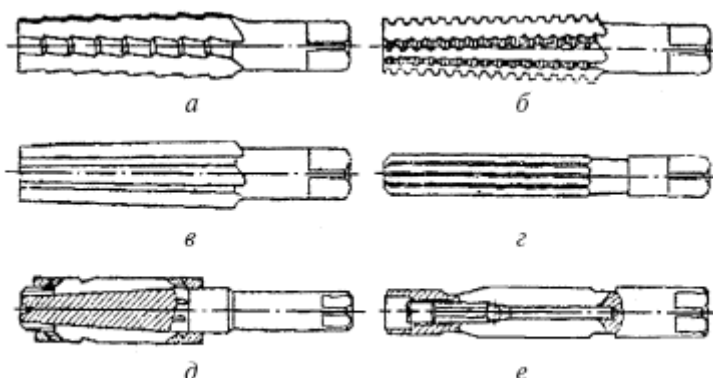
Развертки: а – коническая черновая; б – коническая промежуточная; в – коническая чистовая; г – цилиндрическая с прямыми зубьями; д – цилиндрическая регулируемая; е – цилиндрическая разжимная
